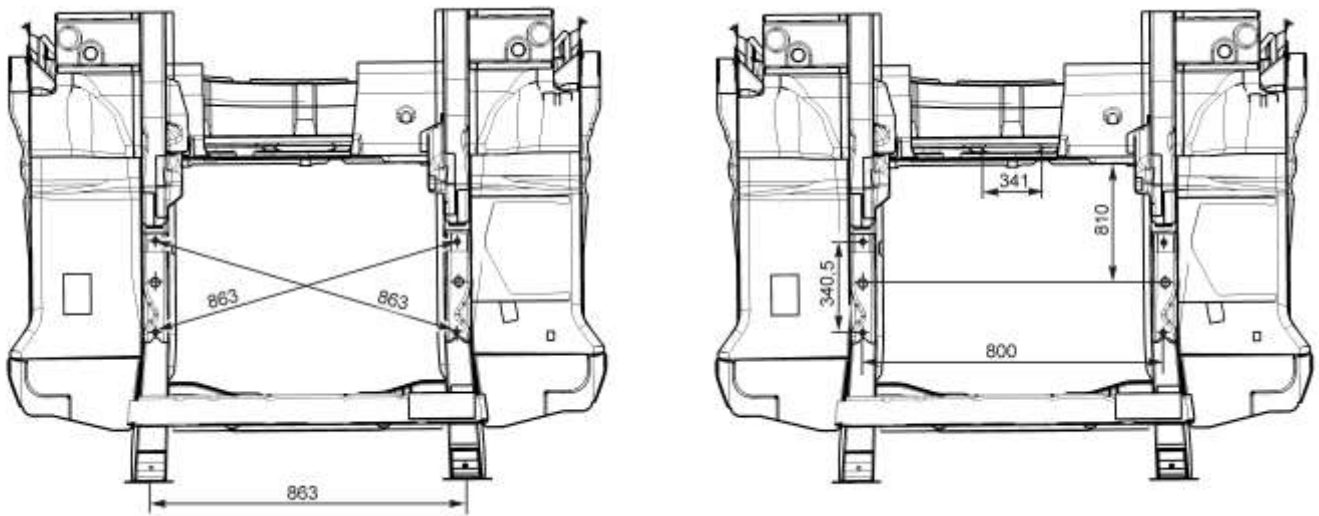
Точки крепления подвесок двигателя (вид снизу).
